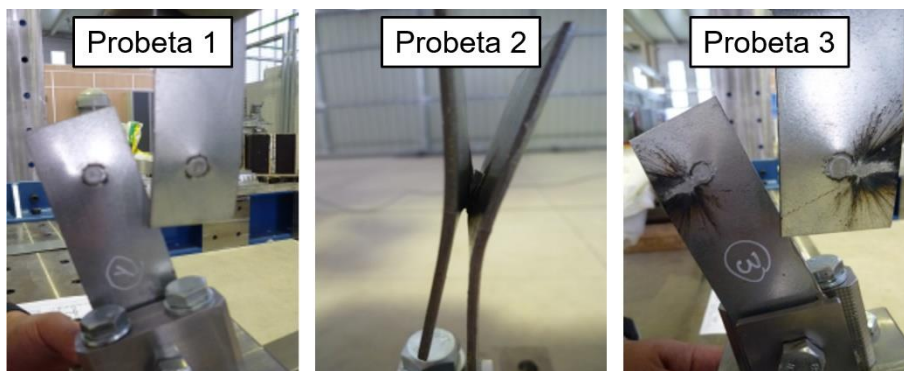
Modos de fallo de los puntos de soldadura de las probetas ensayadas
